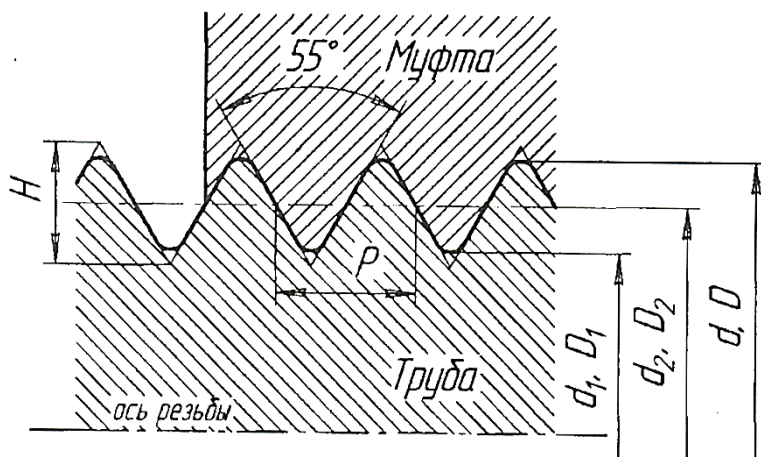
Профиль трубной цилиндрической резьбы
